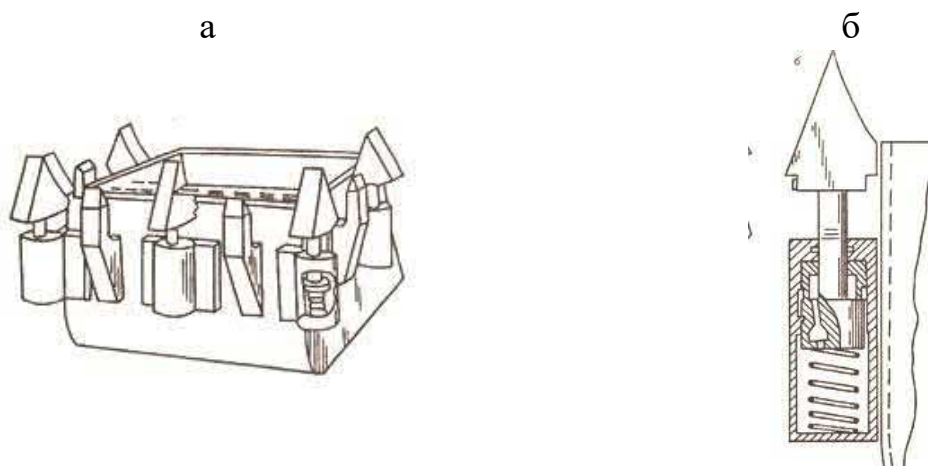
Ковш роторного экскаватора с виброзубьями (патенту № 3550960 США) а – общий вид, б – виброзуб
